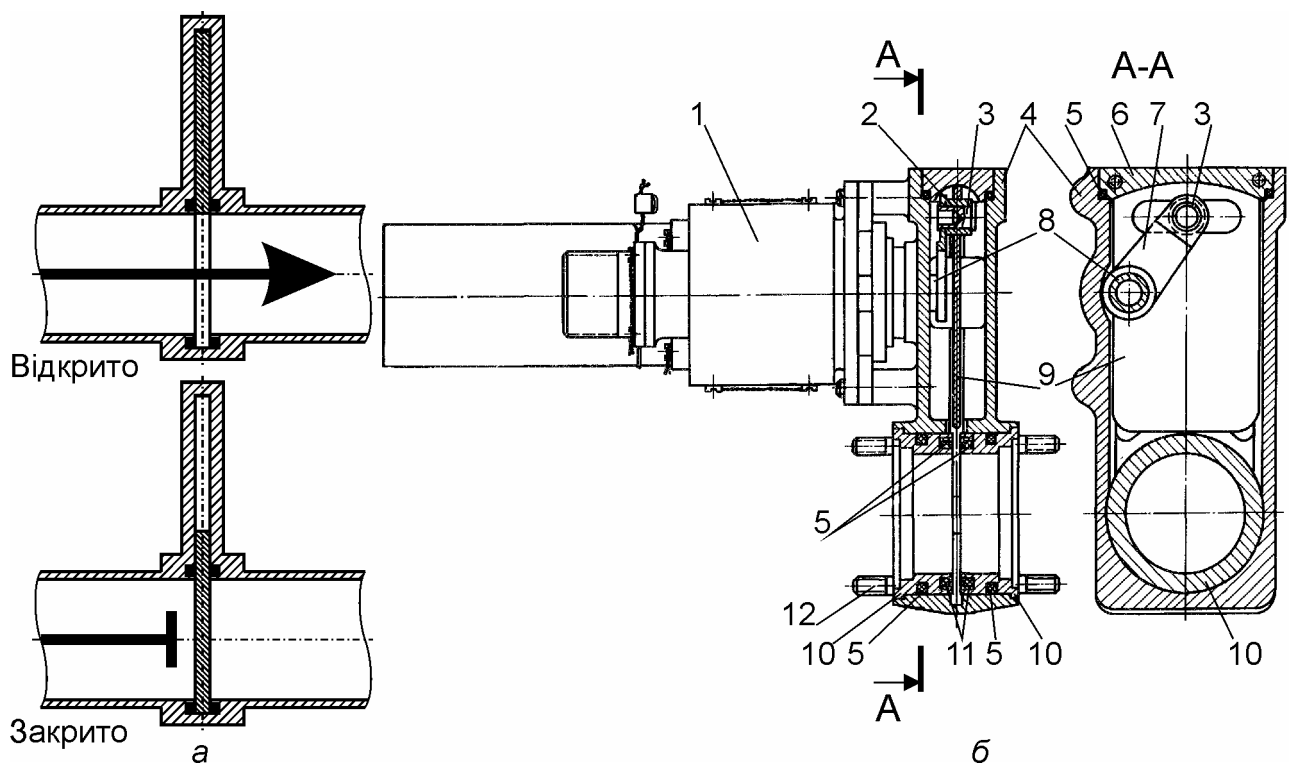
Дисковий кран 768600МА: а — схема роботи; б — конструкція; 1 — електромеханізм; 2 — валець; 3 — поводок; 4 — корпус; 5 — гумові ущільнення; 6 — кришка; 7 — важіль; 8 — вал; 9 — заслінка; 10 — сидла; 11 — сталеві притискні кільця; 12 — шпилька
